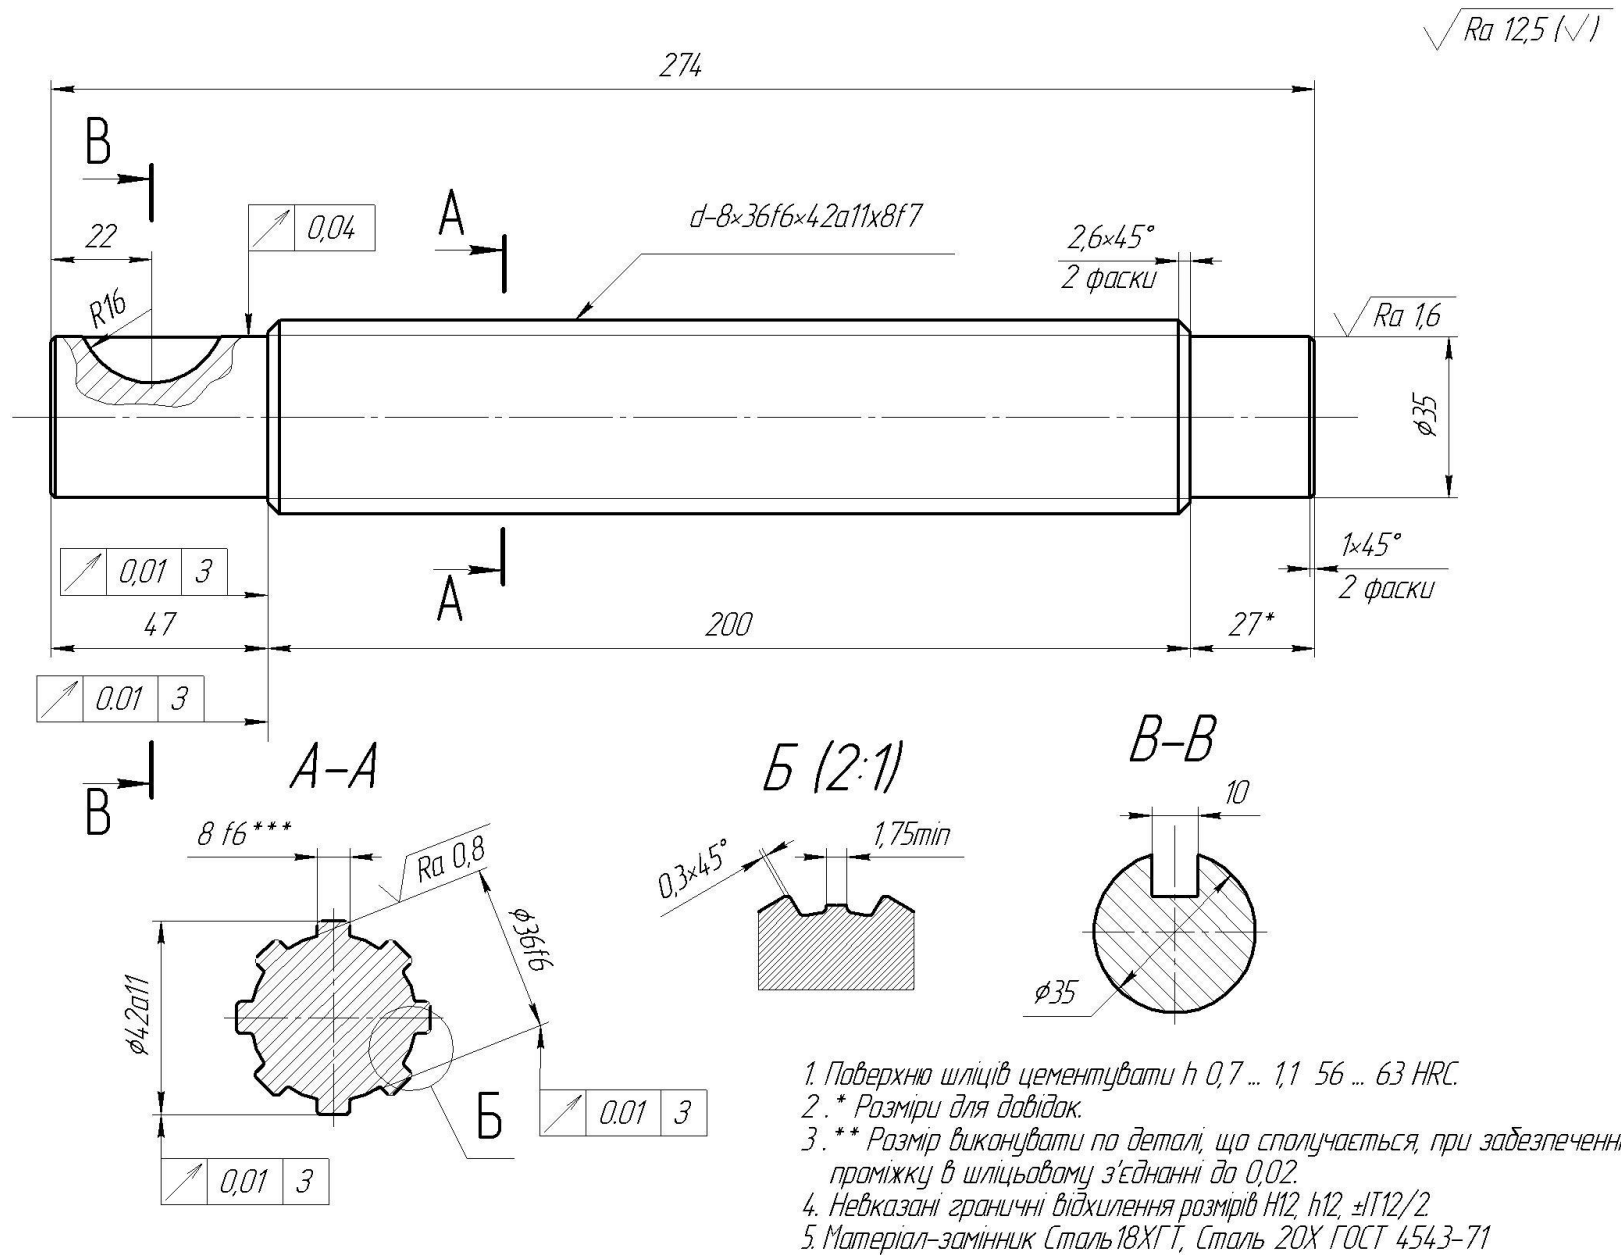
Кресленник деталі «Вал шліцьовий»
